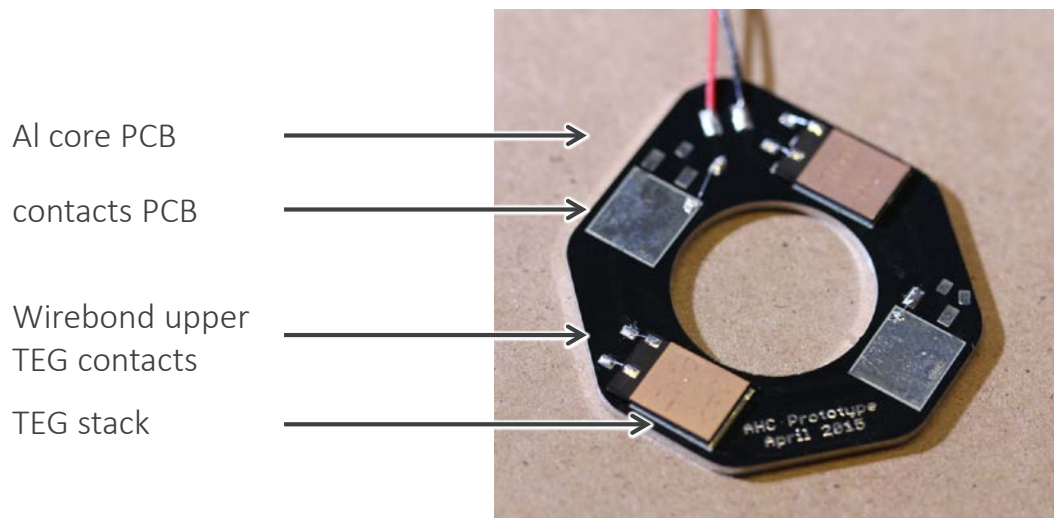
Zwei TEG Stapel welche thermisch und elektrisch auf ein Aluminium-Kern-PCB gelötet wurden. Das PCB wurde speziell für die Integration in das Heizungsventil entworfen.
